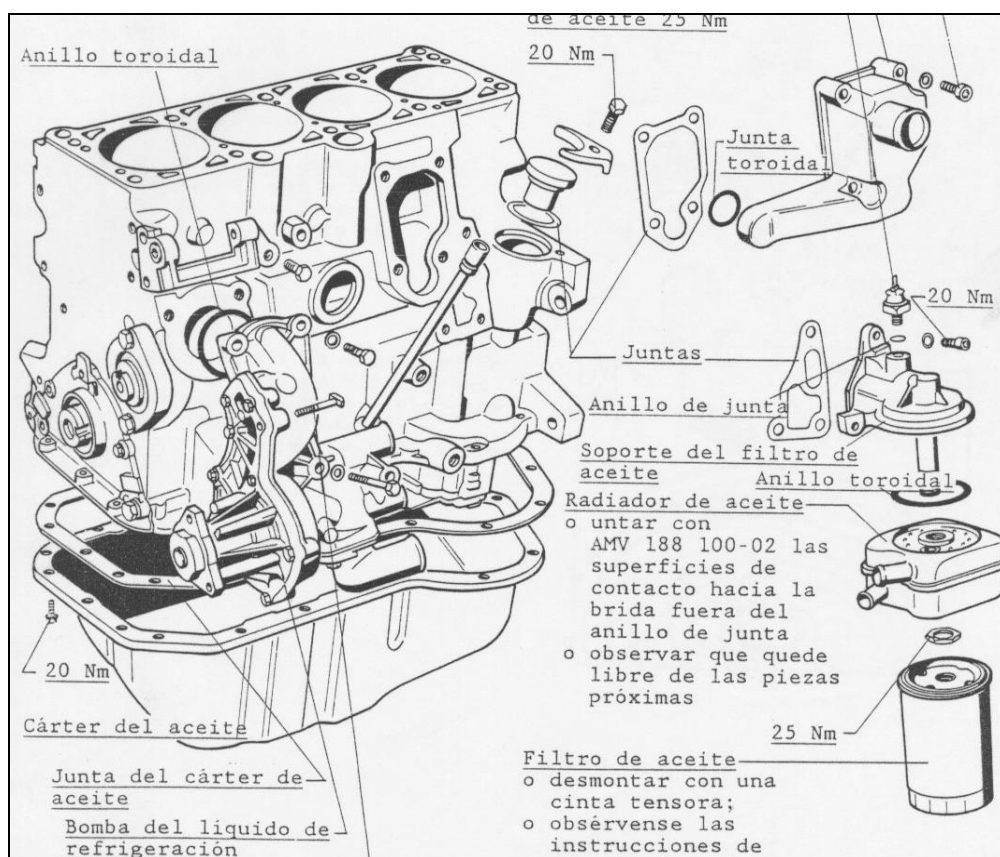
3 Partes principales del sistema de lubricación y refrigeración del motor
